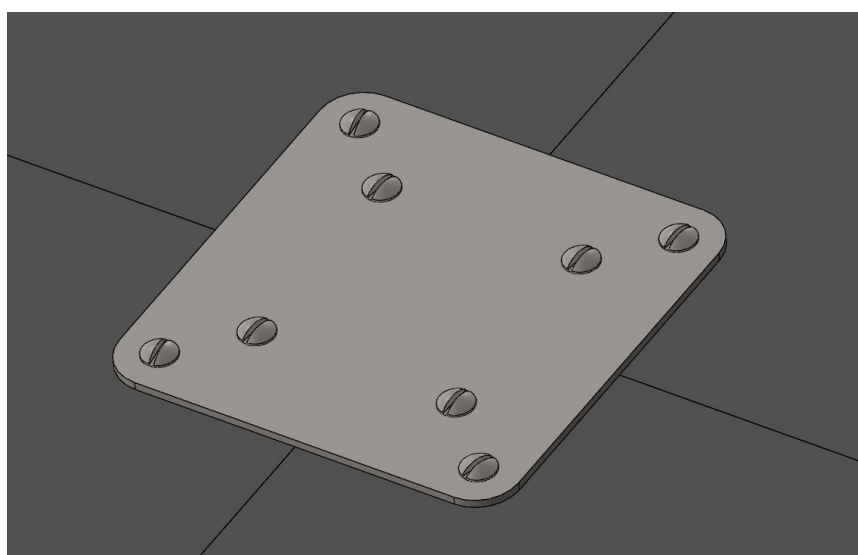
Detalle de las planchuelas para la sujeción de las partes del piso.
